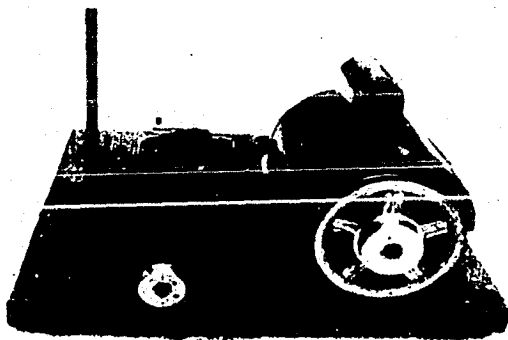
ENSAMBLE DEL MOTOR Y LAS POLEAS.
